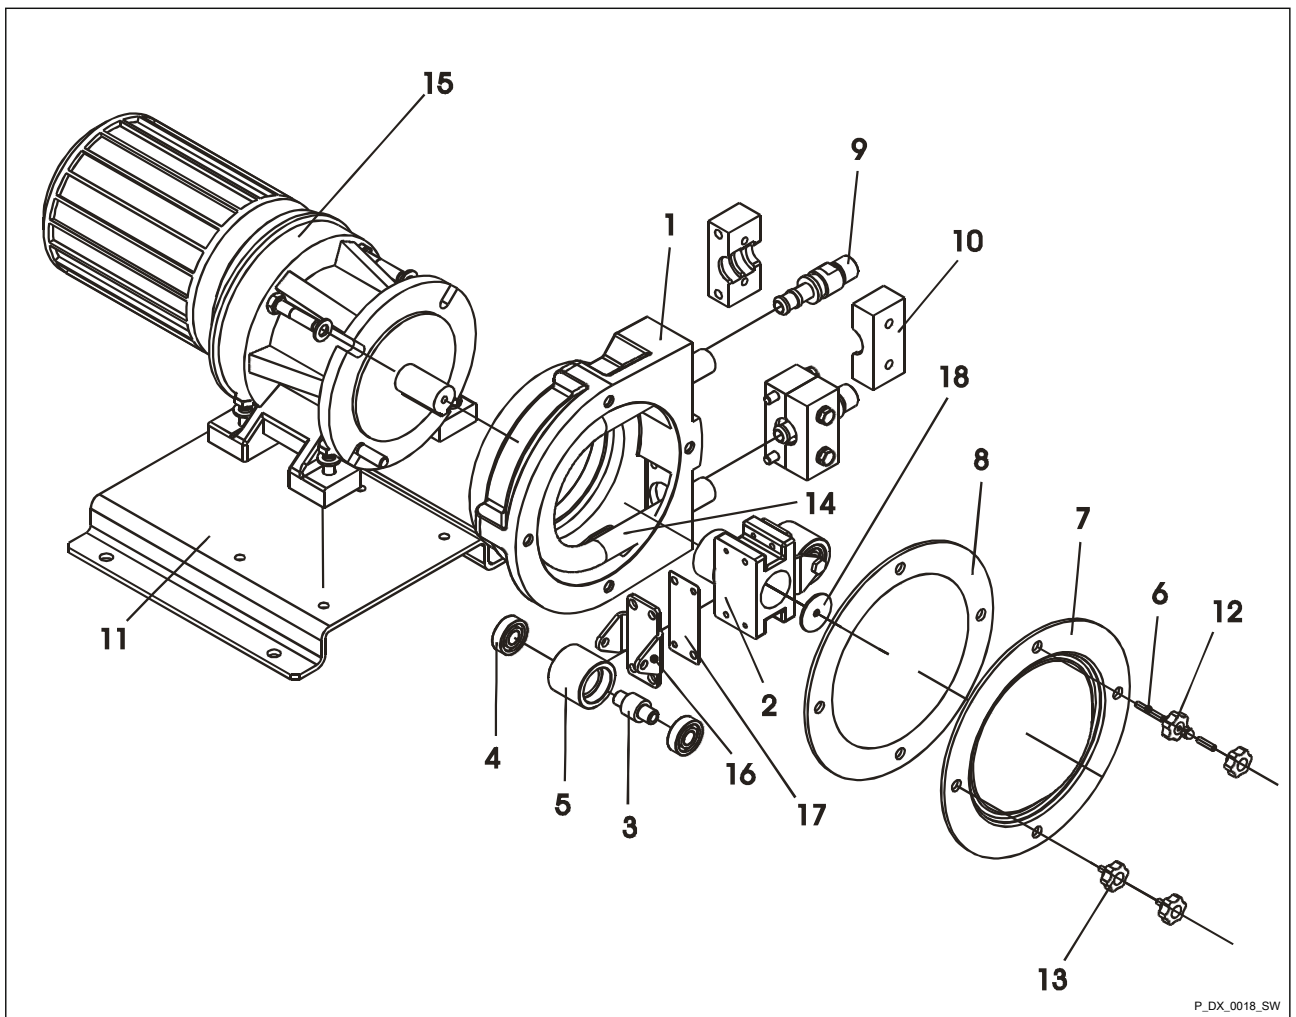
Explosionszeichnung Ersatzteile DFBa 010/013
